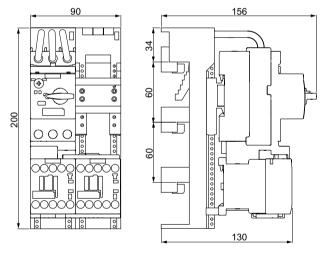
Arrancador inversor S00, AC/DC, bornes de tornillo 3RA2210-..D
